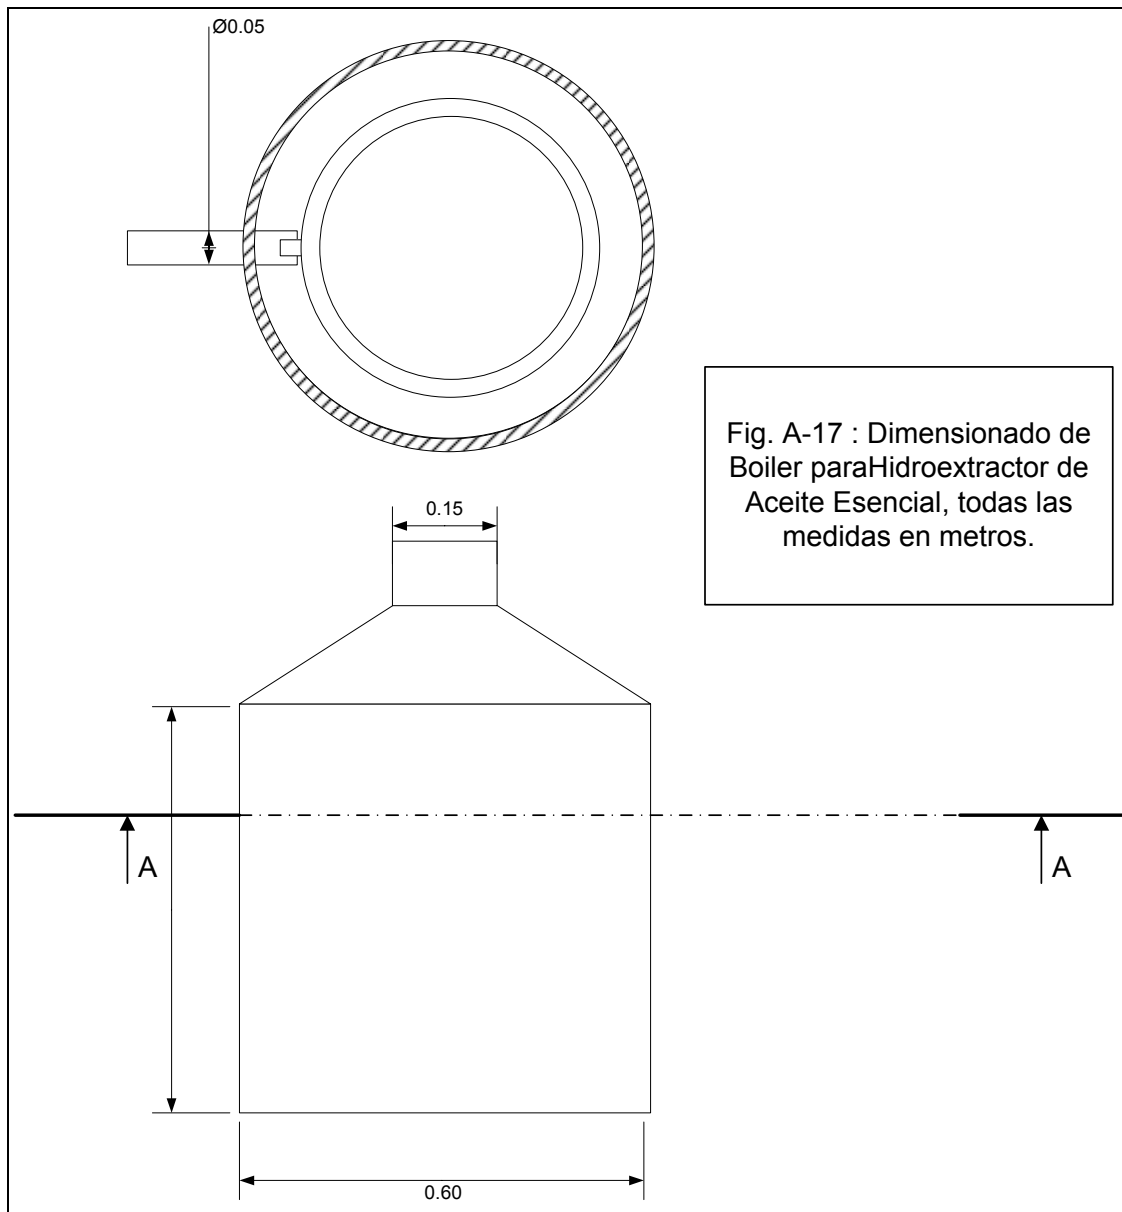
Dimensionado de Boiler para hidroextractor de aceite esencial.
